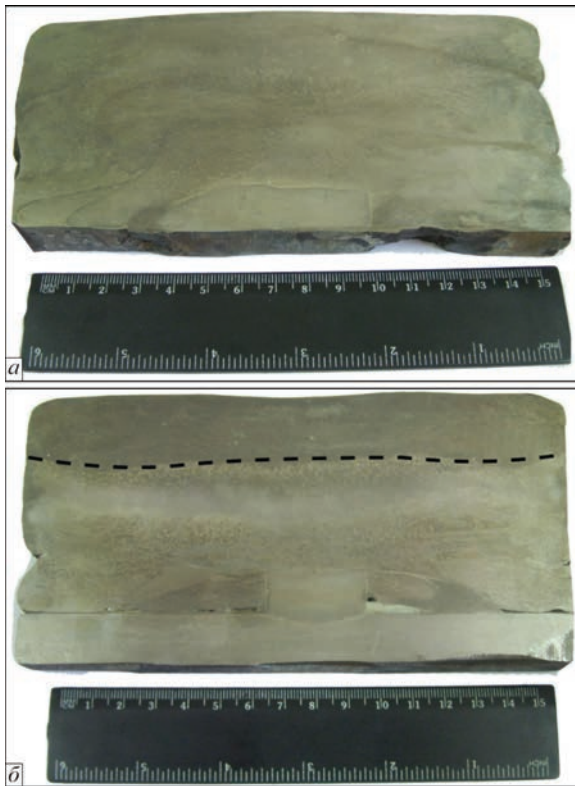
Продольный макрошлиф биметаллической заготовки, полученной наплавкой электродом диаметром 90 мм при  $N_{\text{тпк}} = 80...90$  (а) и  $130...135$  кВ·А (б) (штриховой линией обозначена форма металлической ванны в наплавленном металле)
